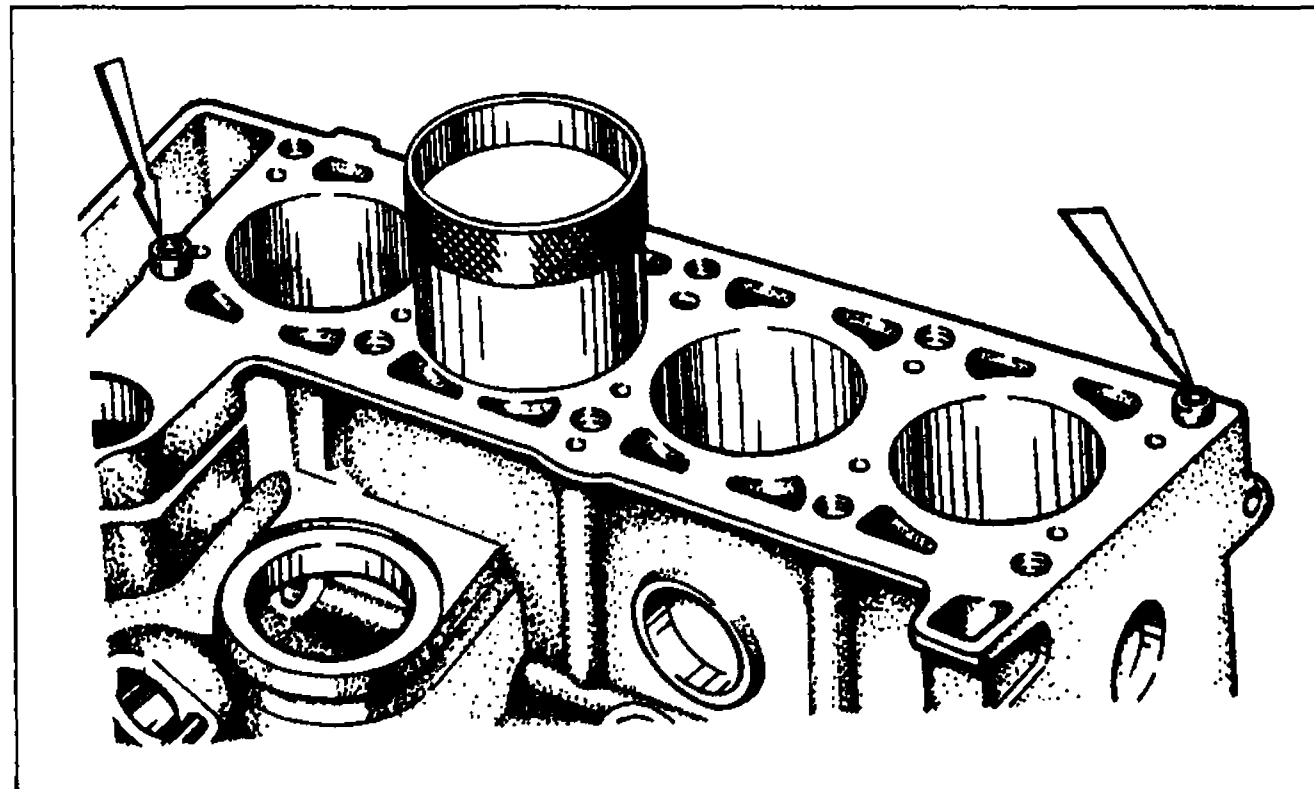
Установка поршня с поршневыми кольцами в цилиндр при помощи монтажной втулки из набора А.60604. Стрелками указаны втулки для центрирования головки на блоке цилиндров
